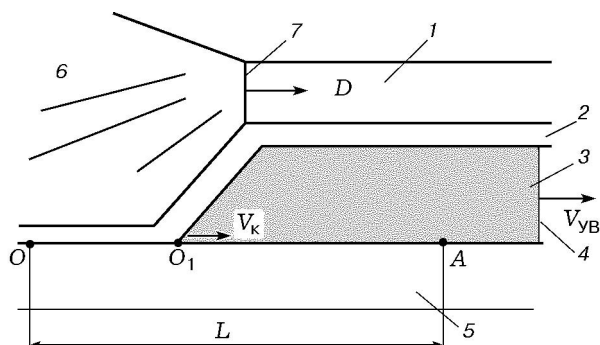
Соударение пластин при сварке взрывом: 1 — слой ВВ; 2 — метаемая пластина; 3 — область сжатого воздуха за фронтом УВ; 4 — фронт УВ; 5 — нижняя пластина; 6 — продукты детонации; 7 — фронт детонации; O — начальная точка сварки; O_1 — точка контакта; A — рассматриваемая точка
